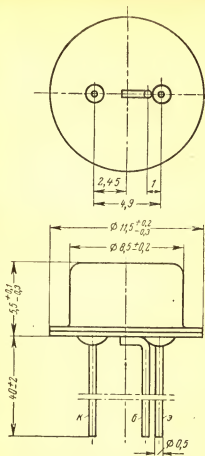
Габаритный чертеж транзисторов П104--П106.
